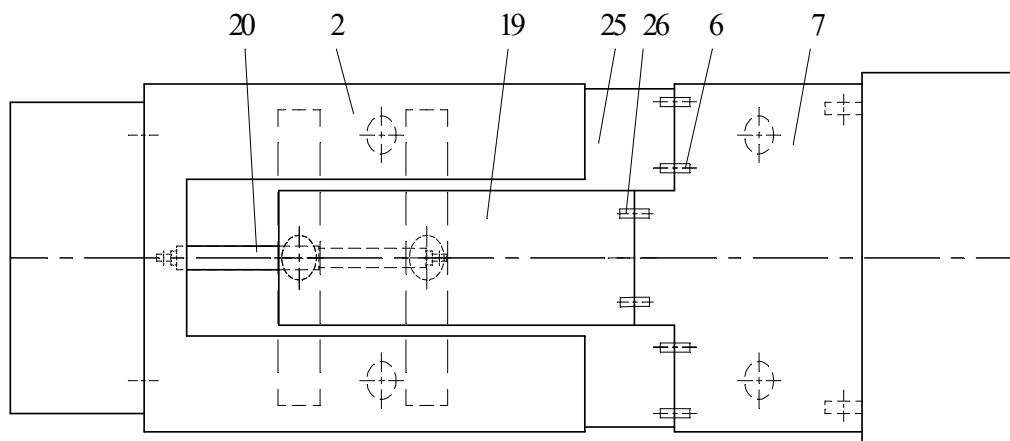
СМК с телескопическими перекрытием и основанием с выдвинутой забойной ступенью перекрытия (вид А сверху на перекрытие)
